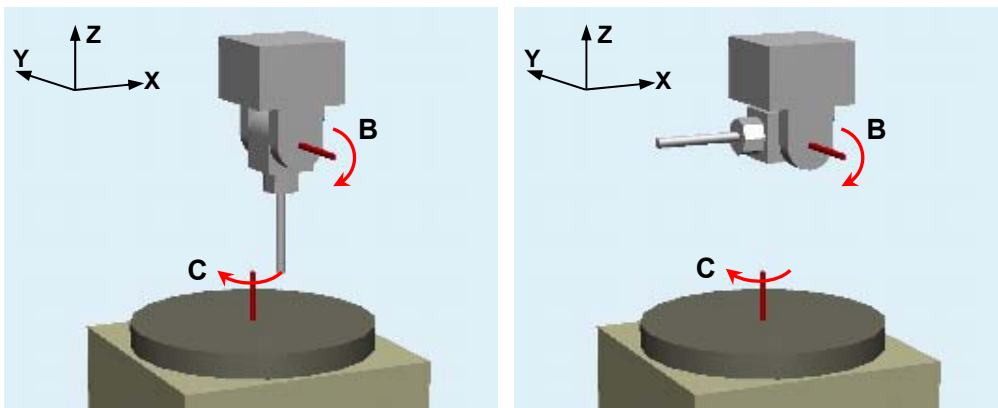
(е) Координаты положения рабочих органов станка B0 C0
